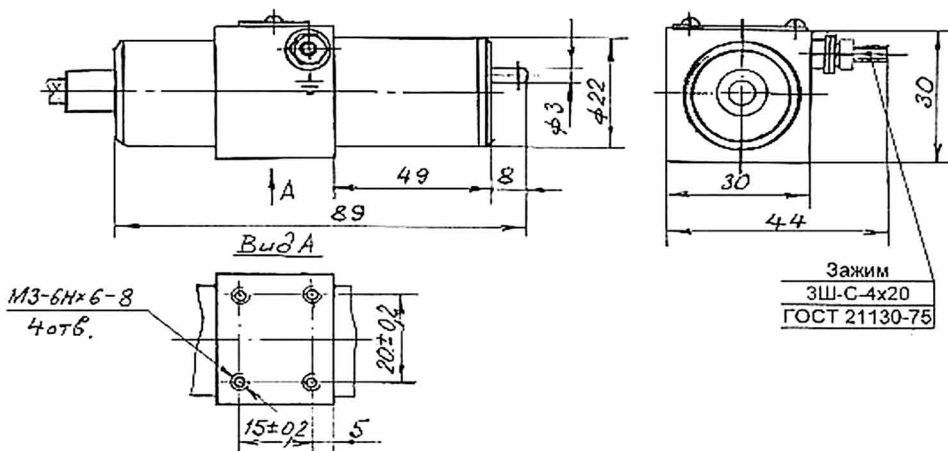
Габаритные и установочные размеры реле РК-301КП
